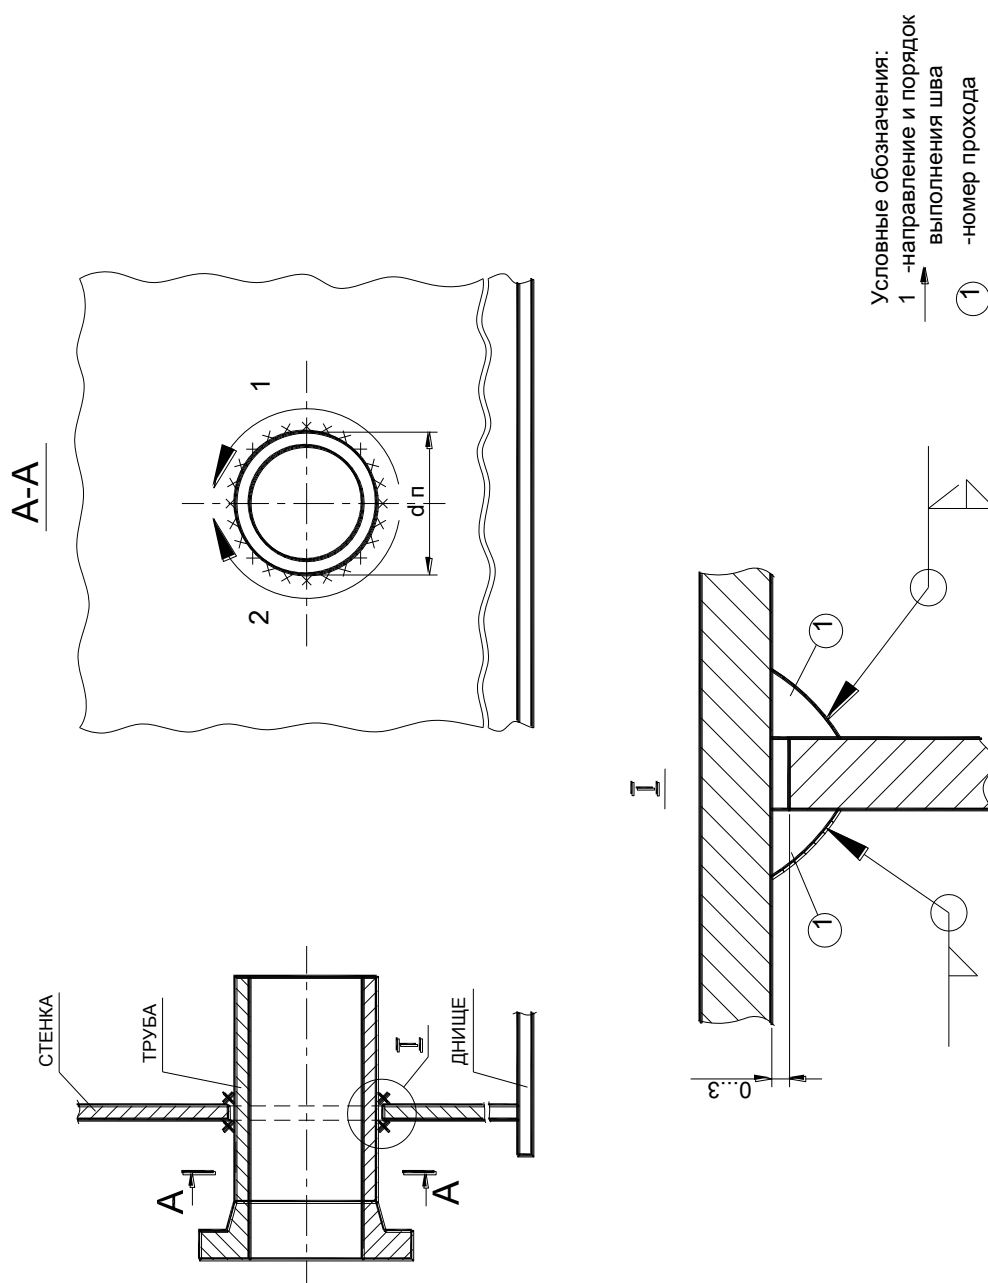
Схема сварки патрубков в стенке без усиливающих листов
